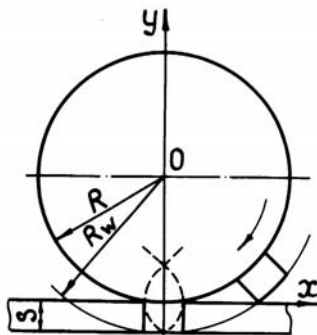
Схема качения вала с пуансоном по полосовой заготовке
